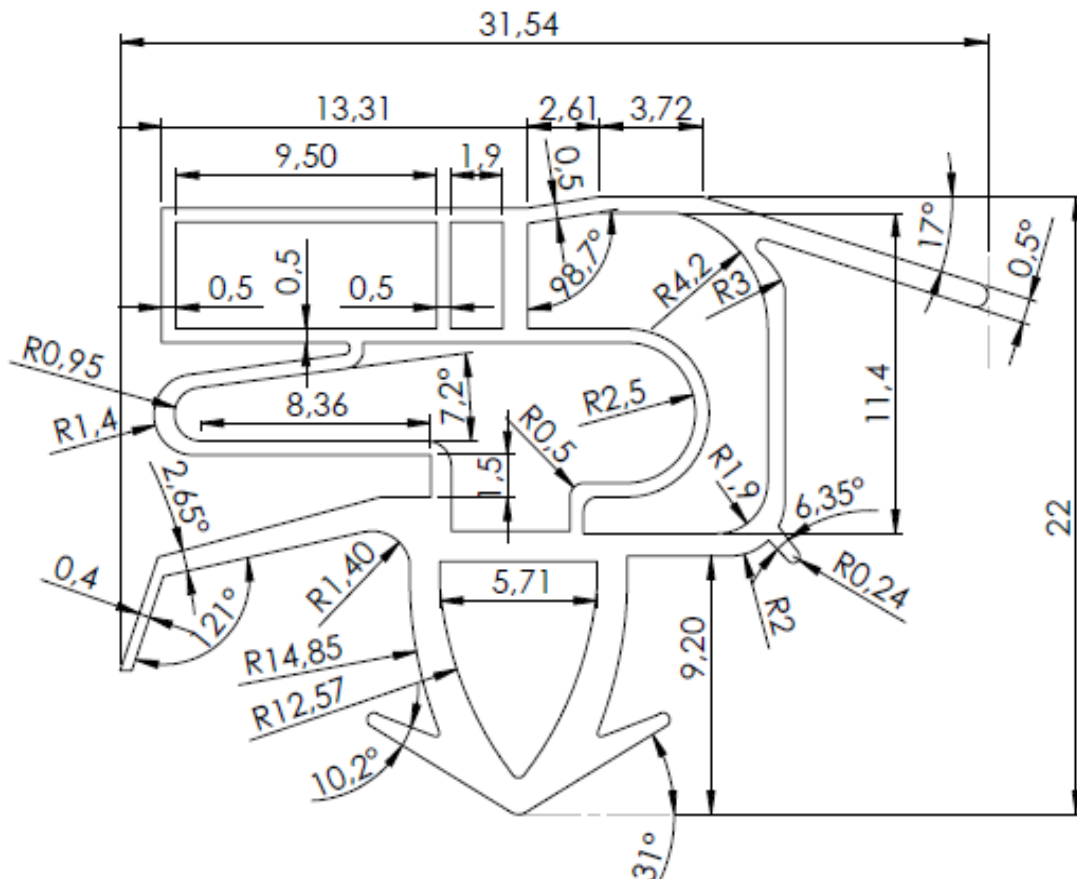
dessin de plan de joint pour la contre porte de congélateur 220F
